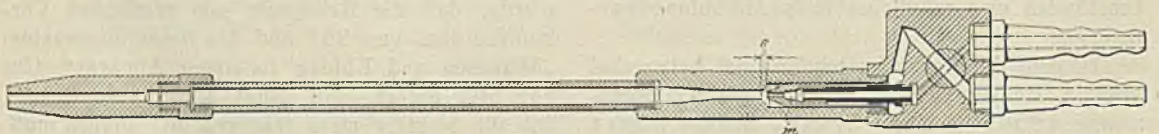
Acetylen-Sauerstoff-Schweißbrenner.
